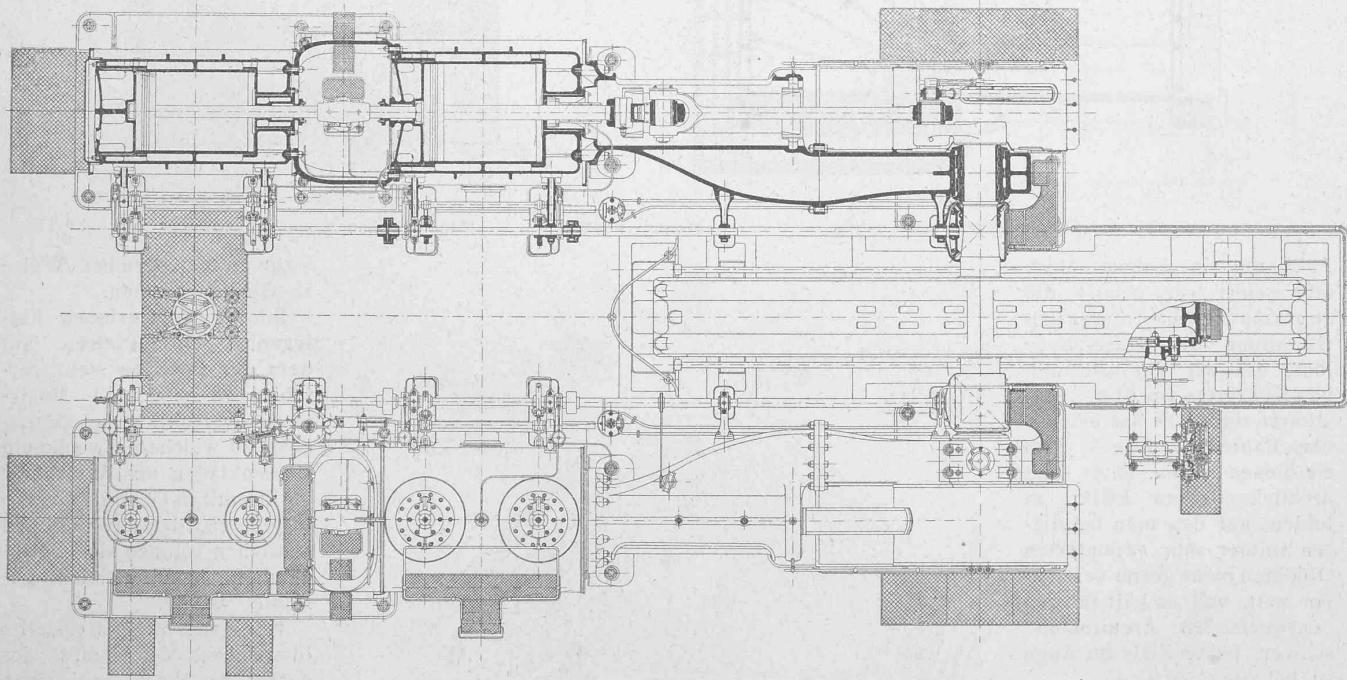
Grundriss. — Schnitt durch die Mitteldruckseite und Ansicht der Hochdruckseite.
